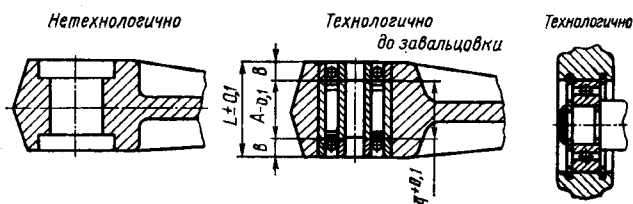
Пример разработки технологичной конструкции ступиц под запрессовку подшипников.
